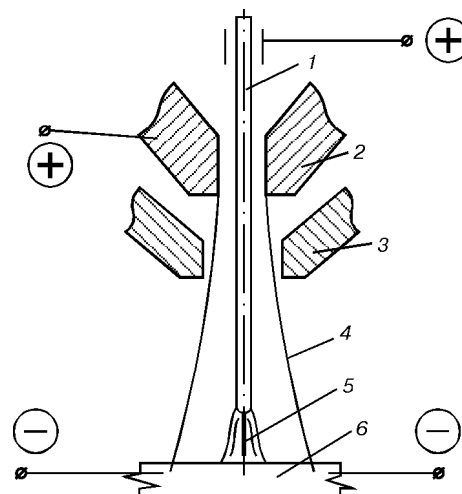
Схема процесса плазма-МИГ сварки (наплавки) (см. обозначения в тексте)
